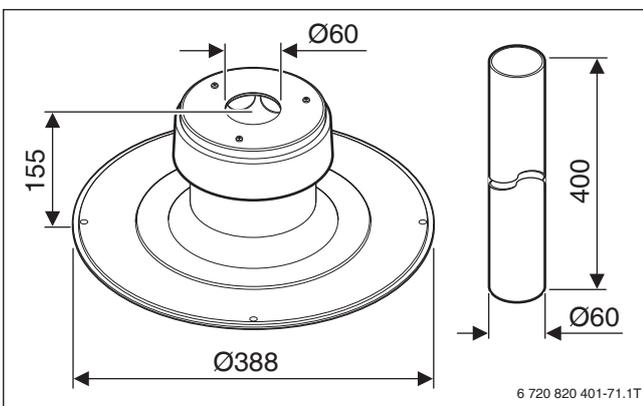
Schachtabdeckung für 60 mm, Aluminium (Maße in mm)
